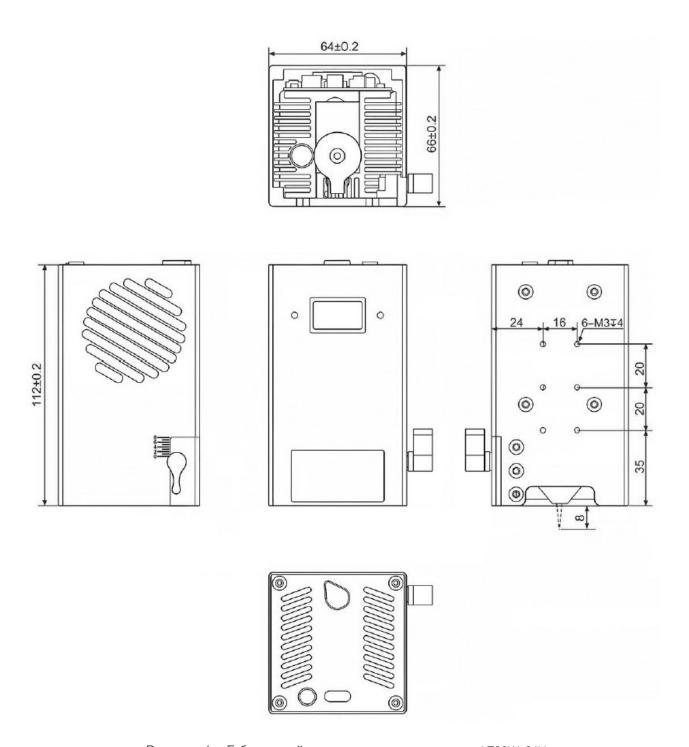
Габаритный чертеж лазерного модуля LT20W-24V.
